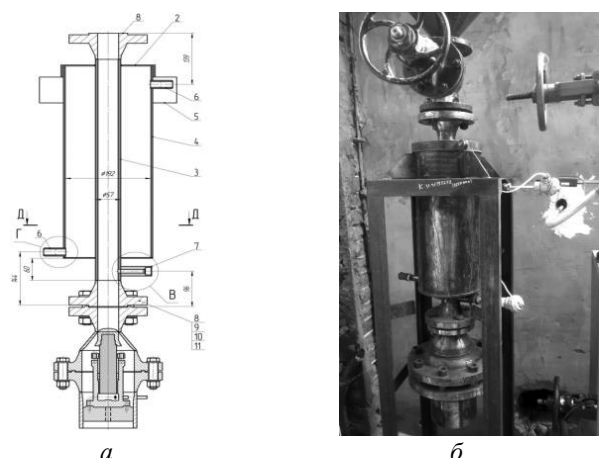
Установка для получения АЛМ и делигнификации: а – сборочный чертеж, б – внешний вид
